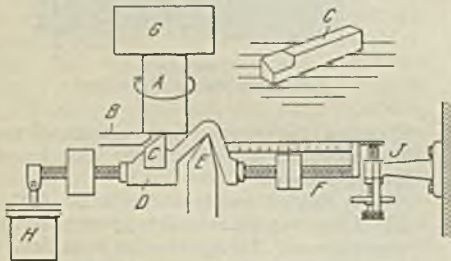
Prüfmaschine für Werkzeugstahl.
